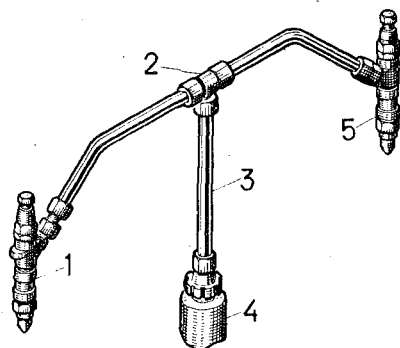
Проверка давления начала впрыскивания топлива по эталонной форсунке:
